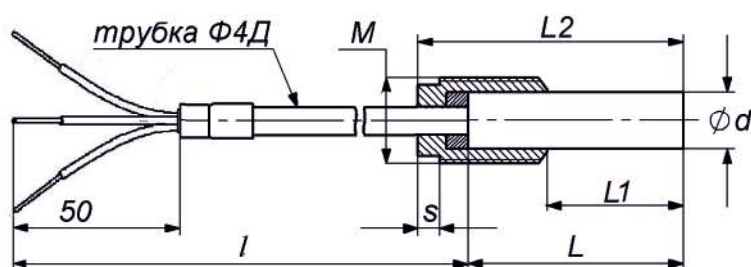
Для измерения температуры подшипников, поверхностей твердых тел и сыпучих материалов. Фторопластовая оболочка для дополнительной герметичности
